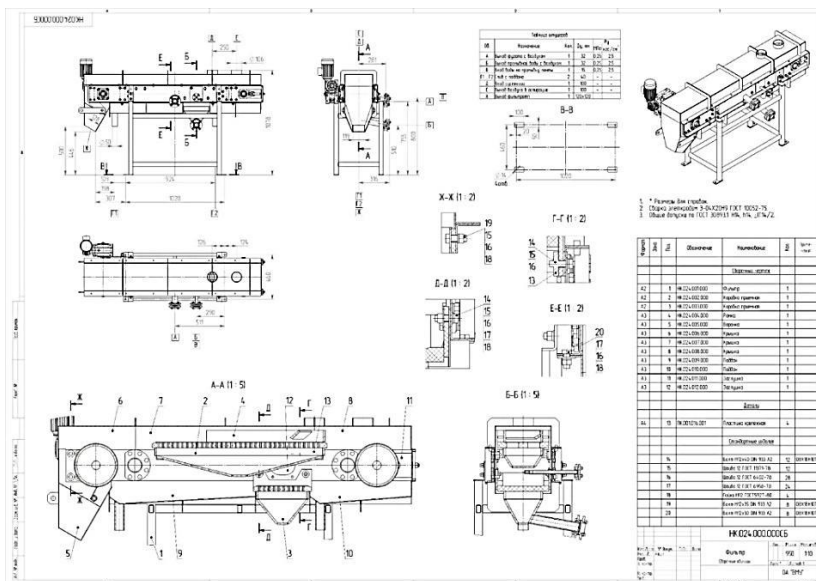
Сборочный чертеж НК 024.000.000 СБ
